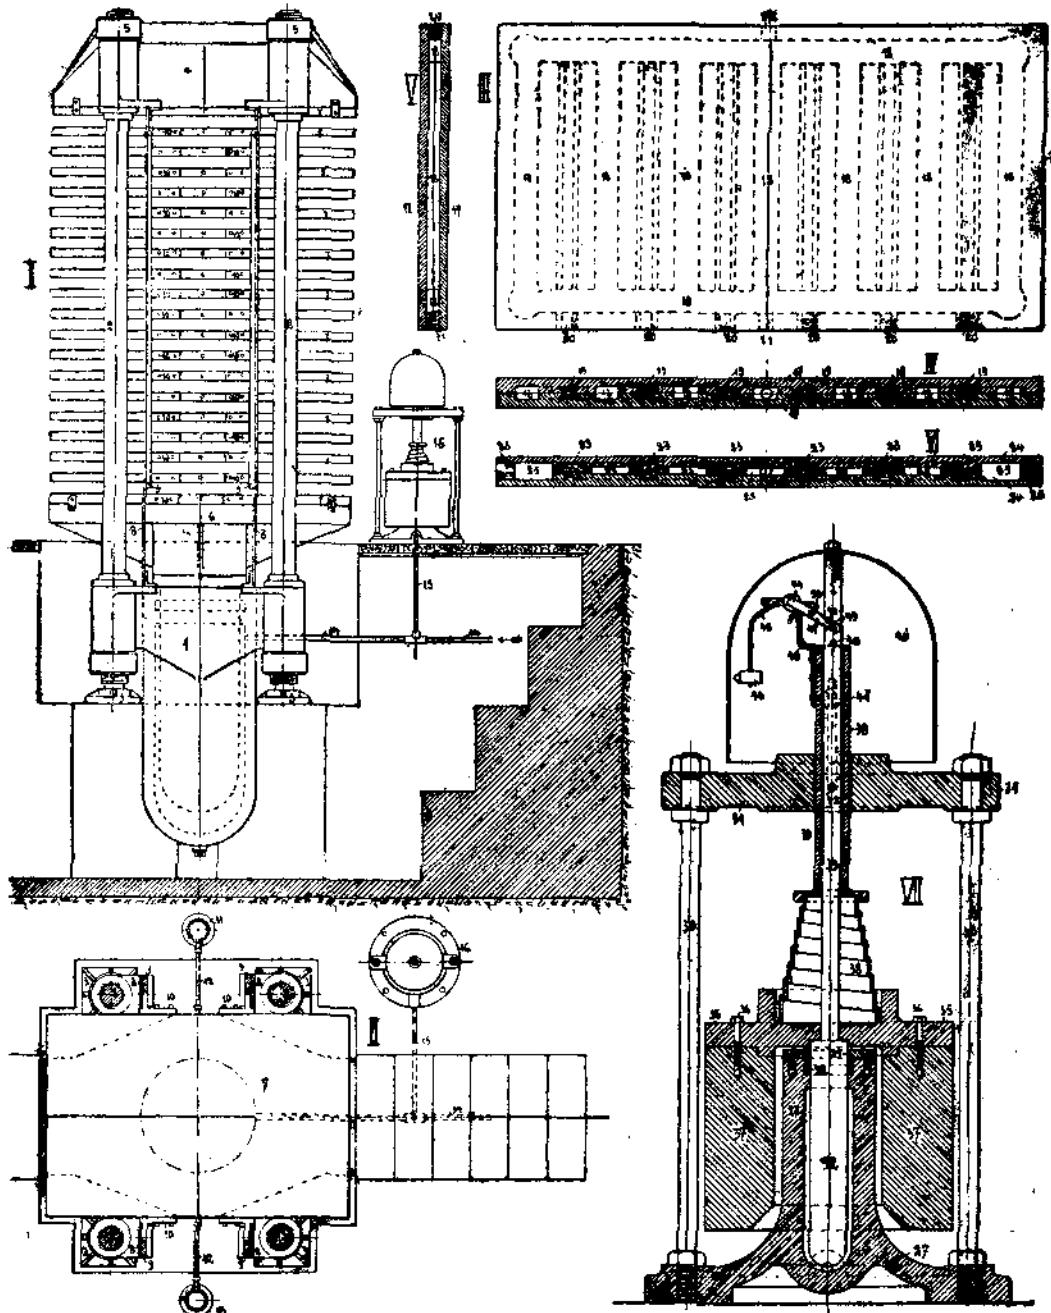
Гидравлический пресс с нагреваемыми паром плитами, усовершенствованный Ниж.-Малиным. I—боковой вид пресса; II—горизонтальный разрез его; III—нагреваемая паром плита; IV—продольный разрез плиты; V—консервный разрез плиты; VI—видоизмененный способ соединения отдельных листов плит; VII—продольный разрез автоматического регулятора.
